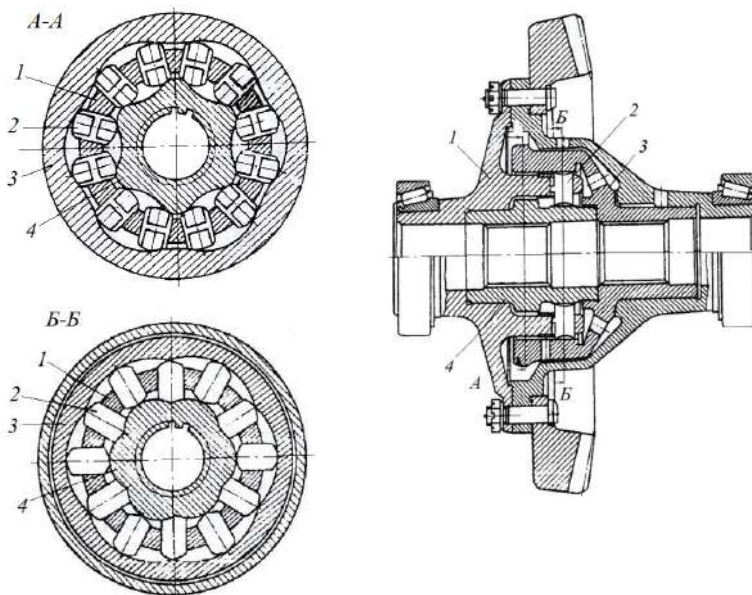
Кулачковий диференціал з радіальним розташуванням кулачків: 1 – сепаратор; 2 – плунжери; 3 – зовнішня зірочка; 4 – внутрішня зірочка
